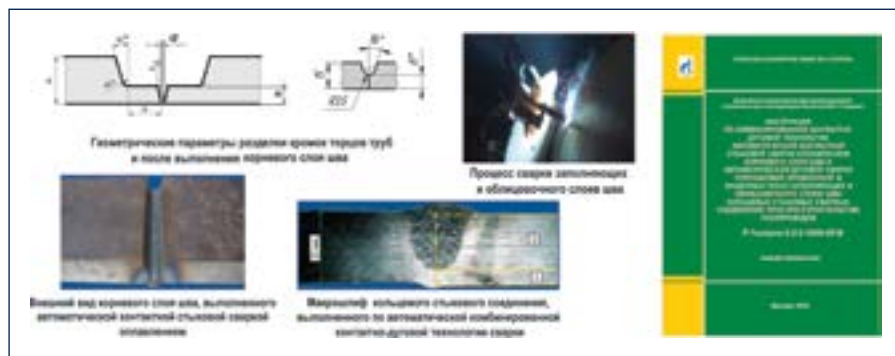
Автоматическая комбинированная контактно-дуговая технология сварки толстостенных труб большого диаметра (корневой слой шва – комплекс типа «КСС» ЗАО «Псковэлектросвар», заполняющие и облицовочный слой шва – автоматическая установка УАСТ-1 производства ООО «НПП «Технотрон»)
